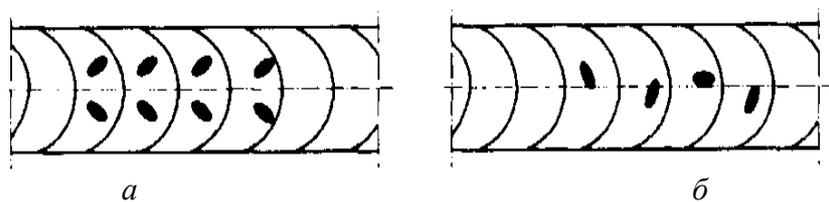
Свищи в сварном шве: *a* – групповые; *б* – одиночные
